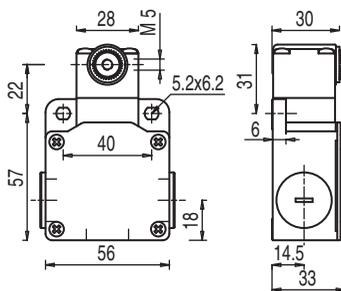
Dimensões do S300-M13C3-M20-CB em mm
